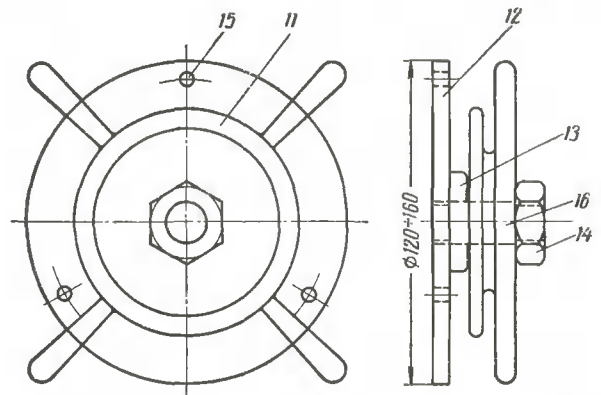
11 — поворотный штурвал; 12 — фланец; 13 — промежуточная шайба; 14 — гайка; 15 — отверстия на фланце (для крепления к стене); 16 — палец.
